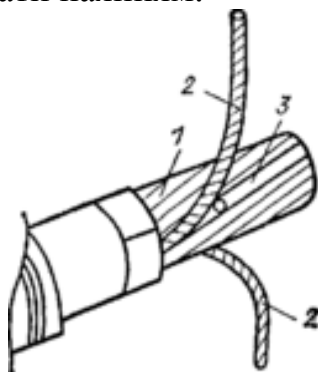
Підготовка кабелю АСБ-2к до зварювання в стик
